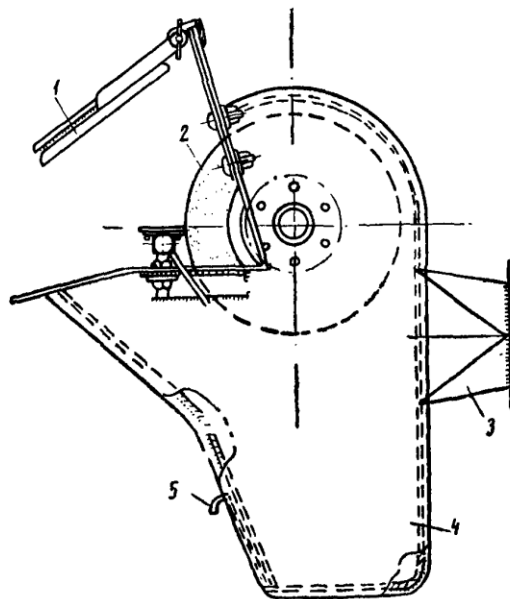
Защитно-знепилюючий витяжний кожух для верстатів ручного заточування інструменту: 1 - захисний екран; 2 - абразивний круг; 3 - відсисаючий повітровід; 4 - пиловідстійник-уловлювач; 5 - засувка
